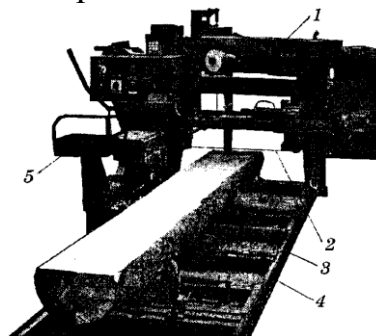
Загальний вигляд горизонтального стрічкопилкового верстата: 1 – пилковий супорт; 2 – стрічкова пилка; 3 – колода; 4 – рама; 5 – робоче місце оператора
